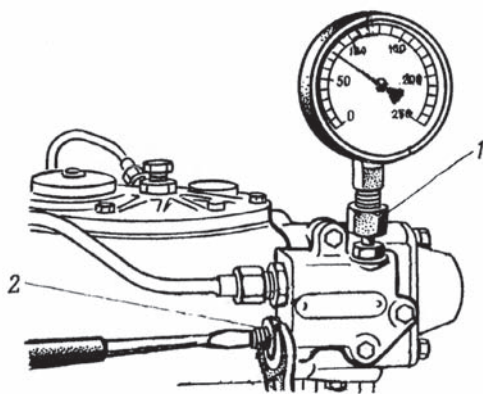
Проверка и регулировка давления срабатывания предохранительного клапана:
